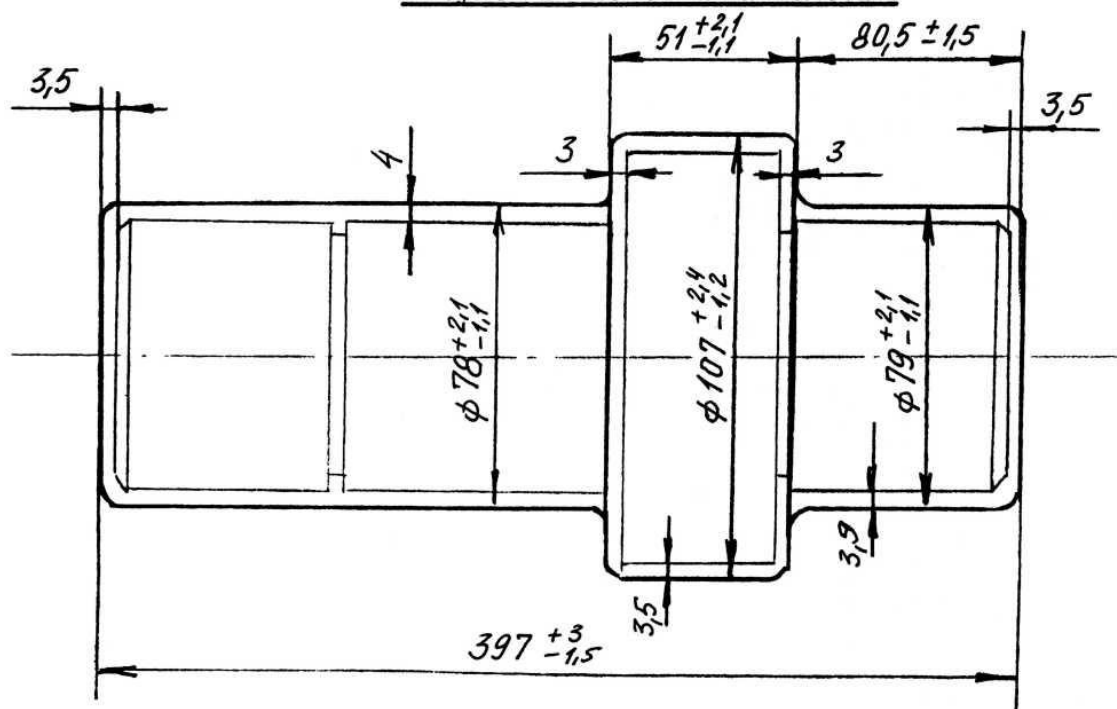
заготовка – поковка, штампованная на ГКМ.
